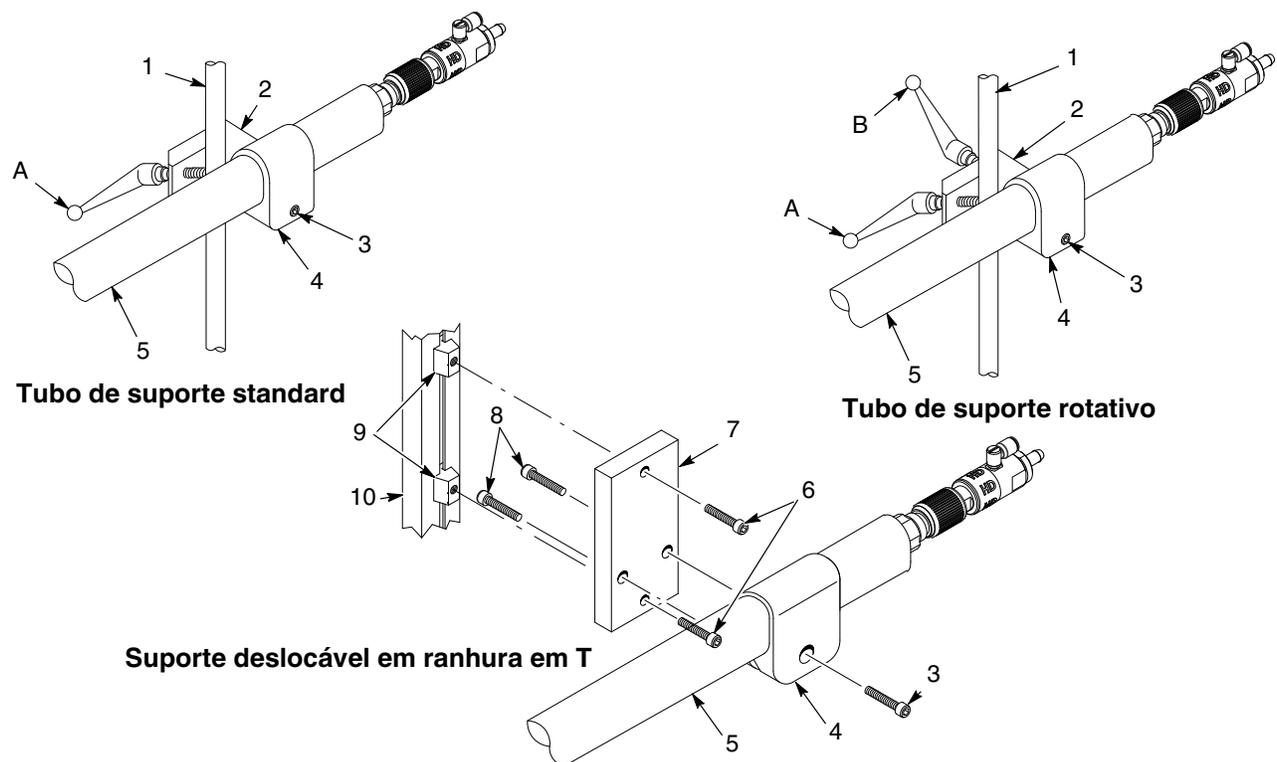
Conjuntos de suporte de pistolas com tubo de suporte
